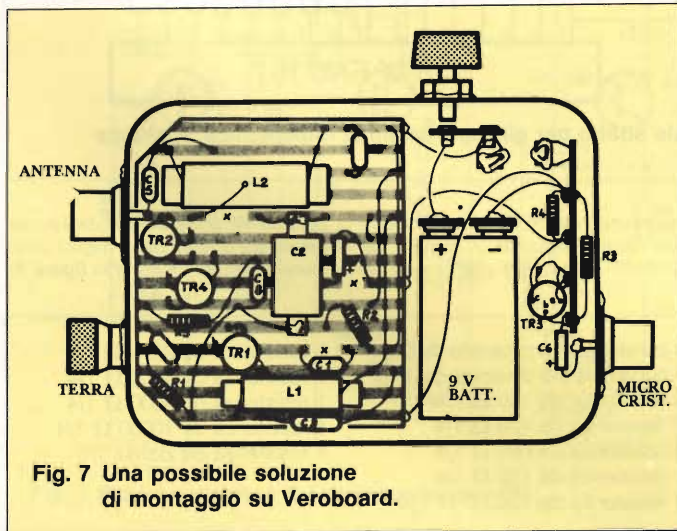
Una possibile soluzione di montaggio su Veroboard.
